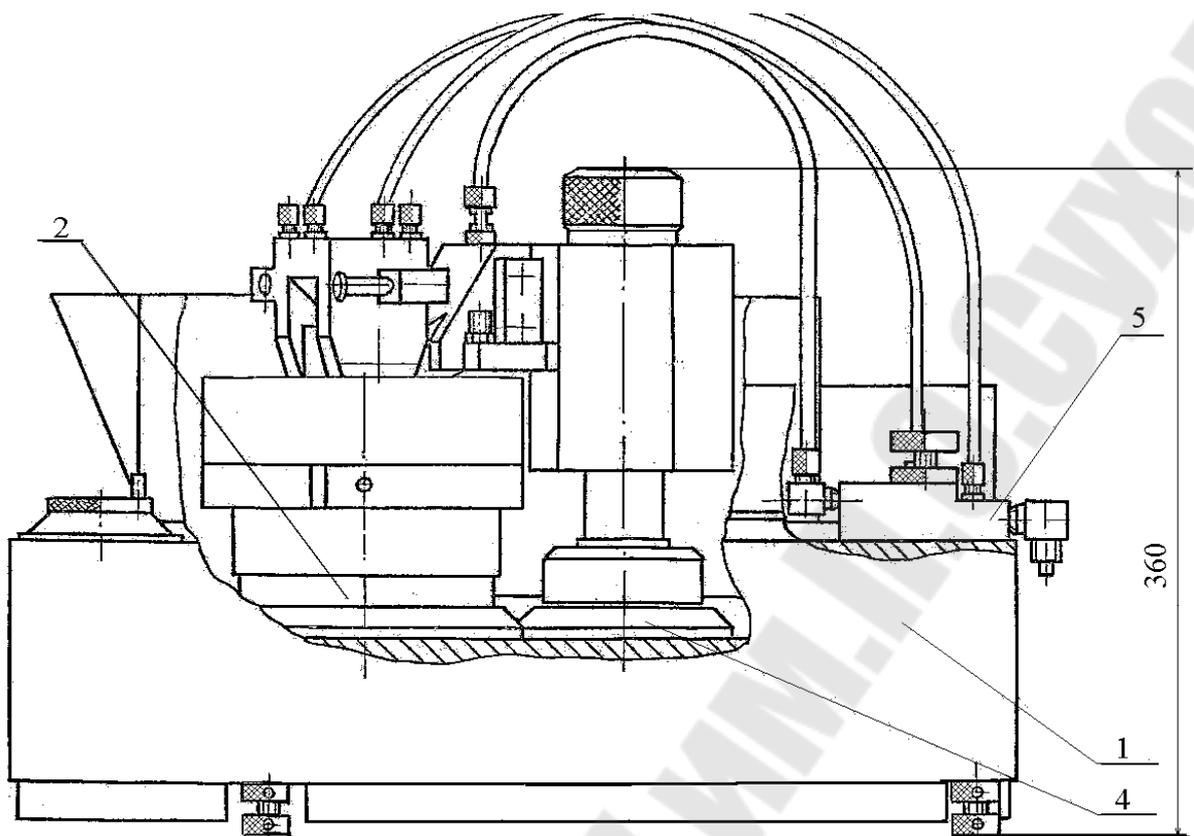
Общий вид шлифовального станка мод. ЗШ4ТМ
